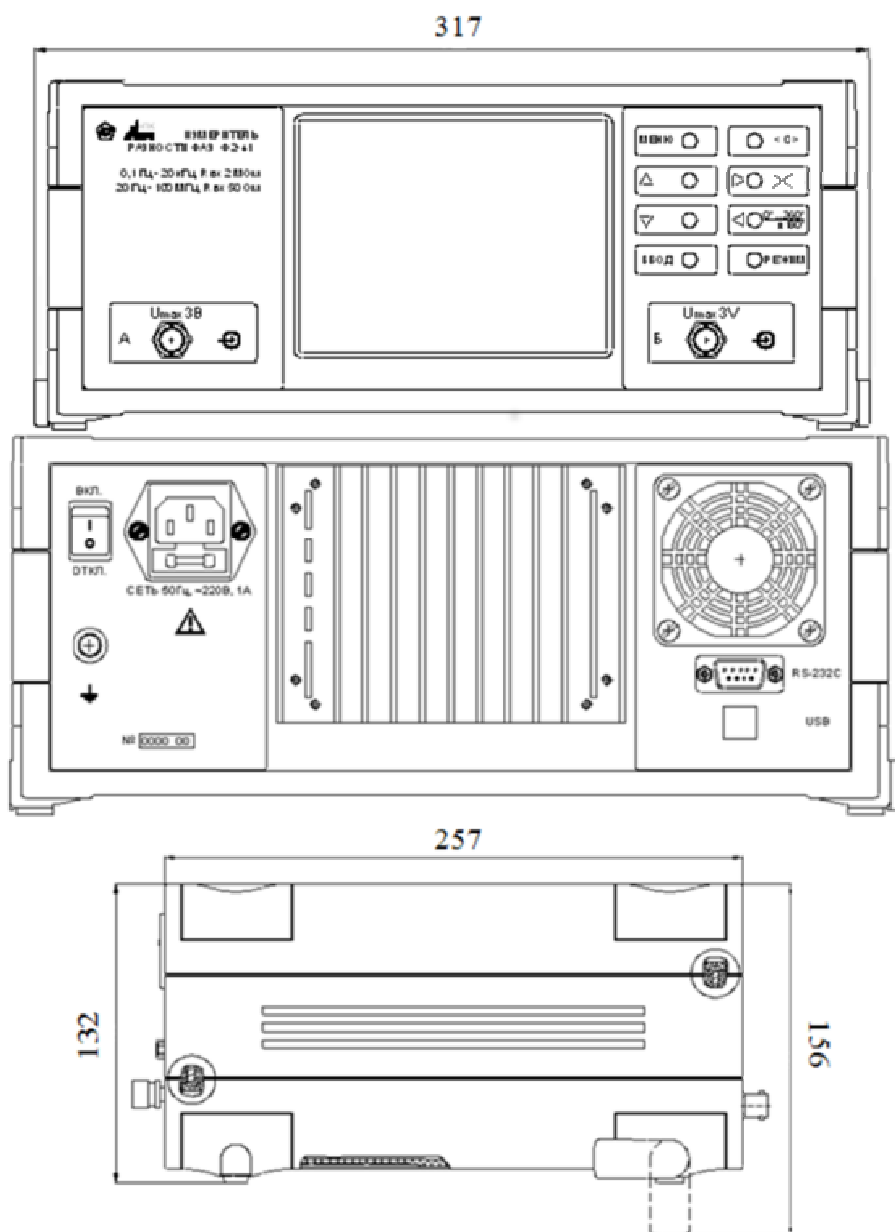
Изображение измерителя разности фаз и габаритные размеры его корпуса
